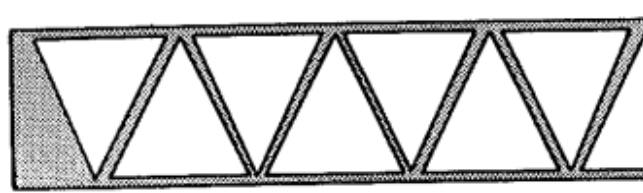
Disposición invertida de la pieza a cortar. Fuente: [2]
